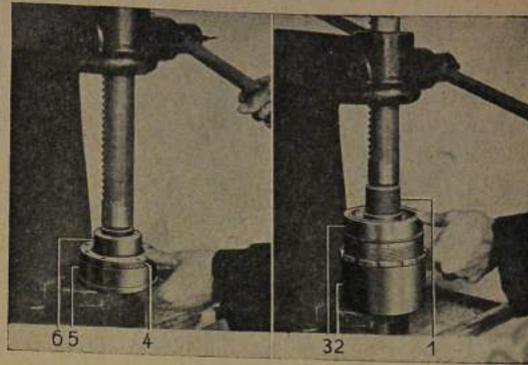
Hochschulterkugellager mit Druckring aus Einstellbuchse herausdrücken
